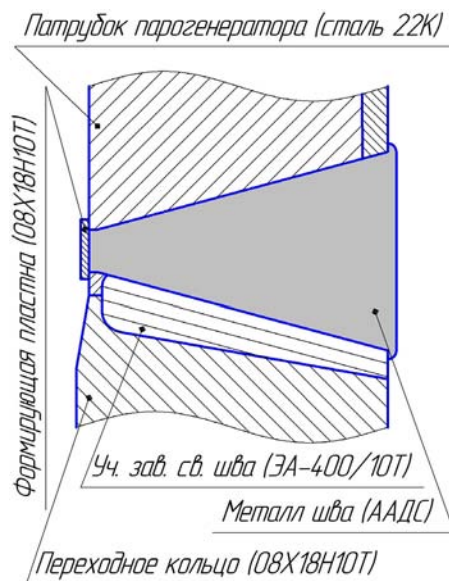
Отремонтированное сварное соединение автоматической сваркой с «узкой разделкой»
